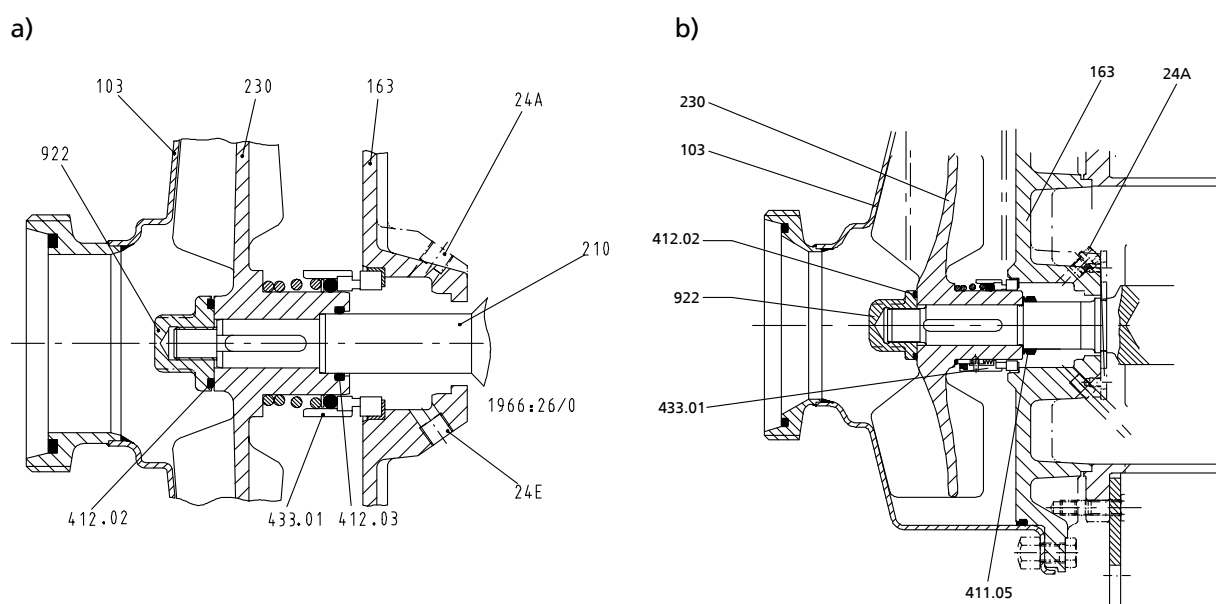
Одинарное торцовое уплотнение а) с кольцом круглого сечения (группа типоразмеров I) б) с кольцом V-образного сечения (группа типоразмеров II)
